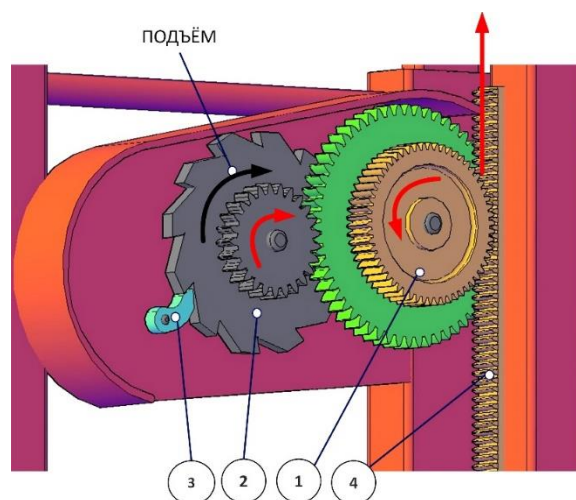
Тележка для транспортировки и монтажа колес габаритной грузовой техники:
